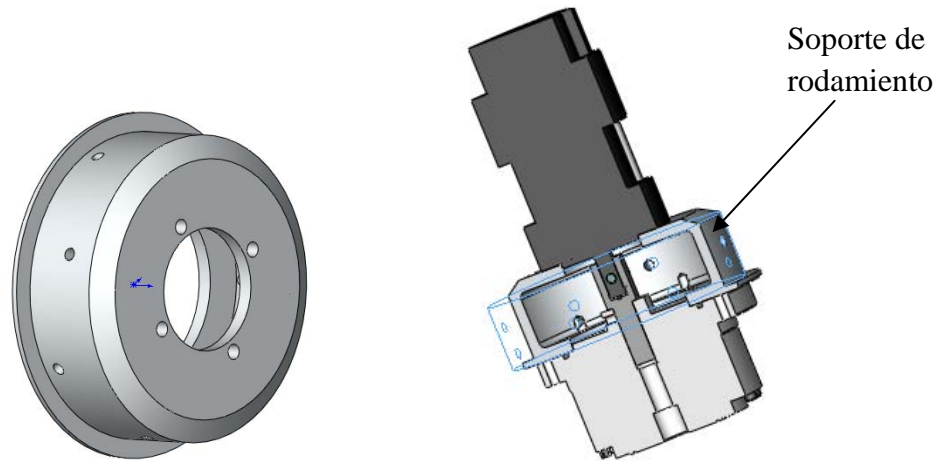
Izqda. vista 3-D de soporte de rodamiento. Dcha. Colocación en el ensamblaje.
